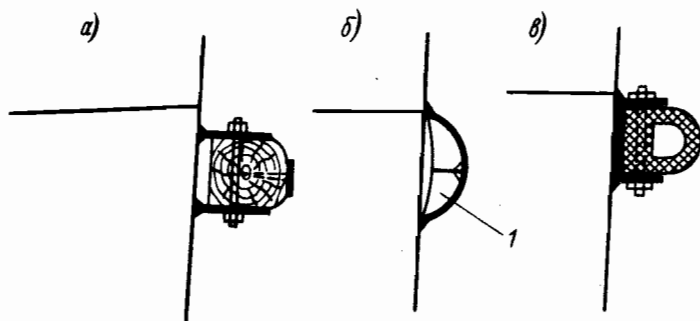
Привальный брус: а — деревянный; б — металлический; в — резино-металлический.
